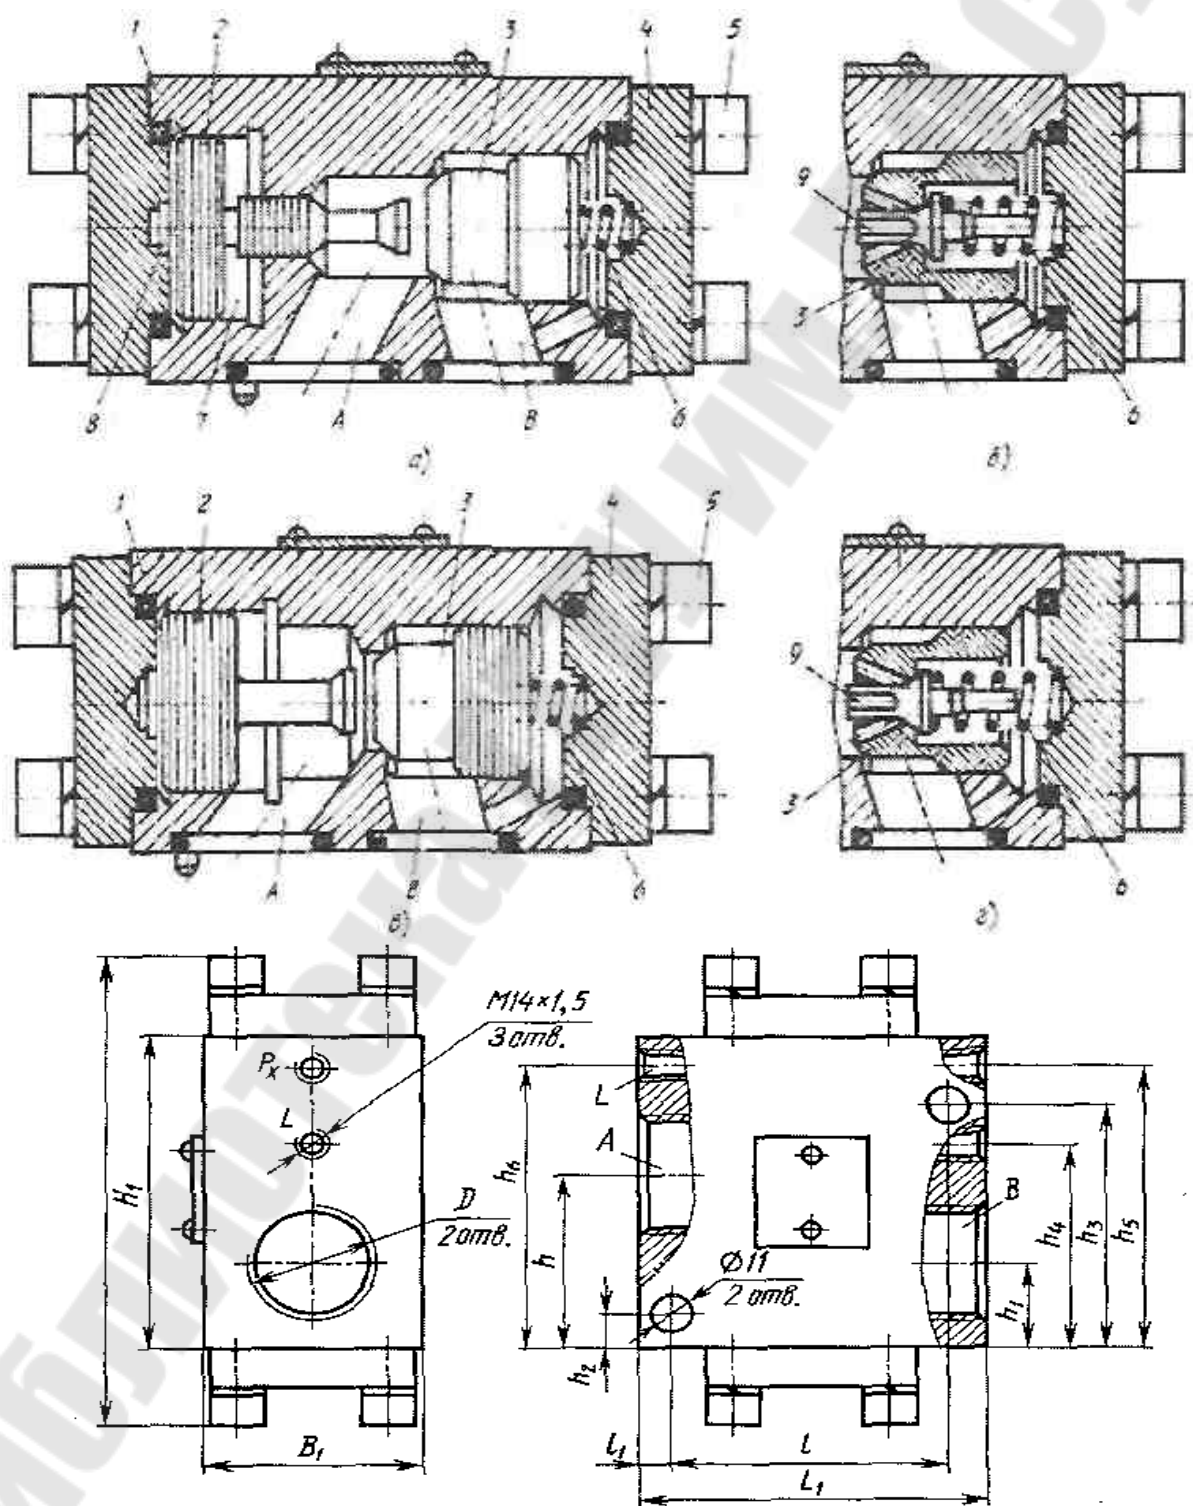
Конструкция и габаритные размеры односторонних гидрозамков типа КУ
